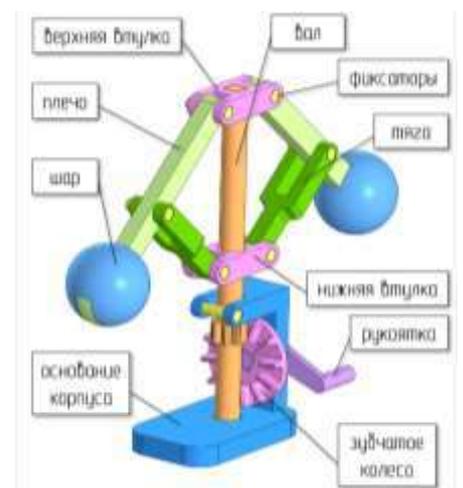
Образец 3D-модели центробежного механизма регулятора Уатта
